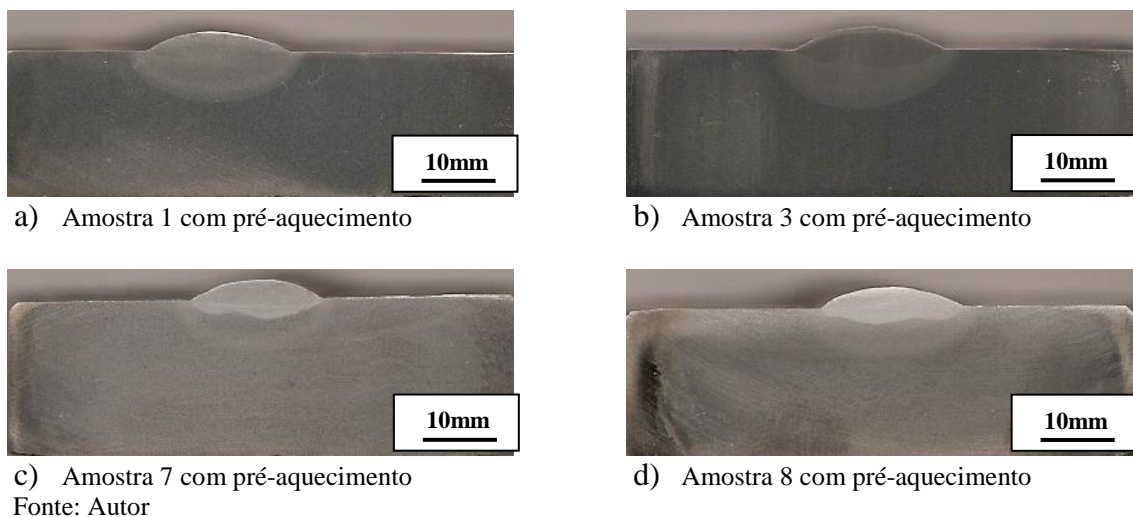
Macrografias dos corpos de prova soldados com pré-aquecimento
